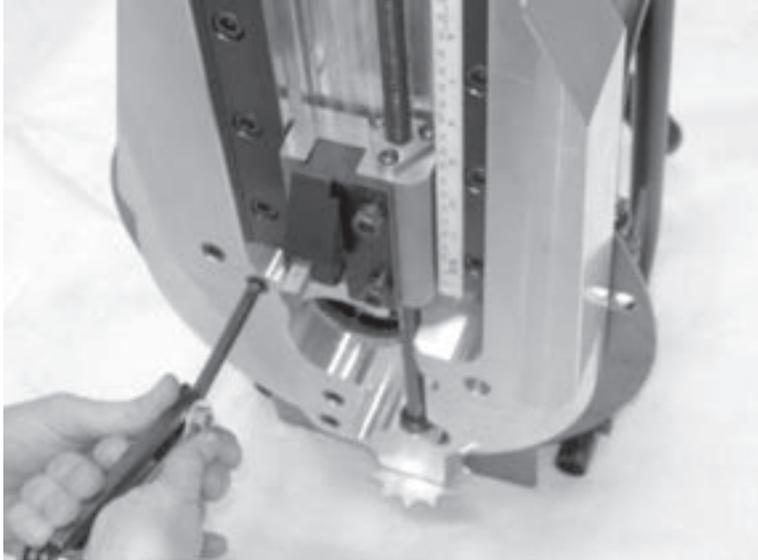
Afloje los 6 tornillos que sujetan el carro portaherramientas de punta única.
